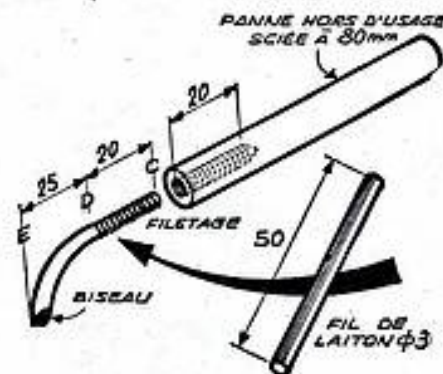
La panne modifiée est apte à réaliser des soudures très délicates. La panne hors d'usage utilisée, a l'avantage de constituer un accumulateur de chaleur (ce qui permet d'utiliser la panne miniature de 3 mm plus longtemps, sans avoir besoin de rebrancher le fer sur le secteur). Cette panne miniature est utilisée sur un fer à panne interchangeable, de 100 watts, semblable à celui de la fig. 1.
